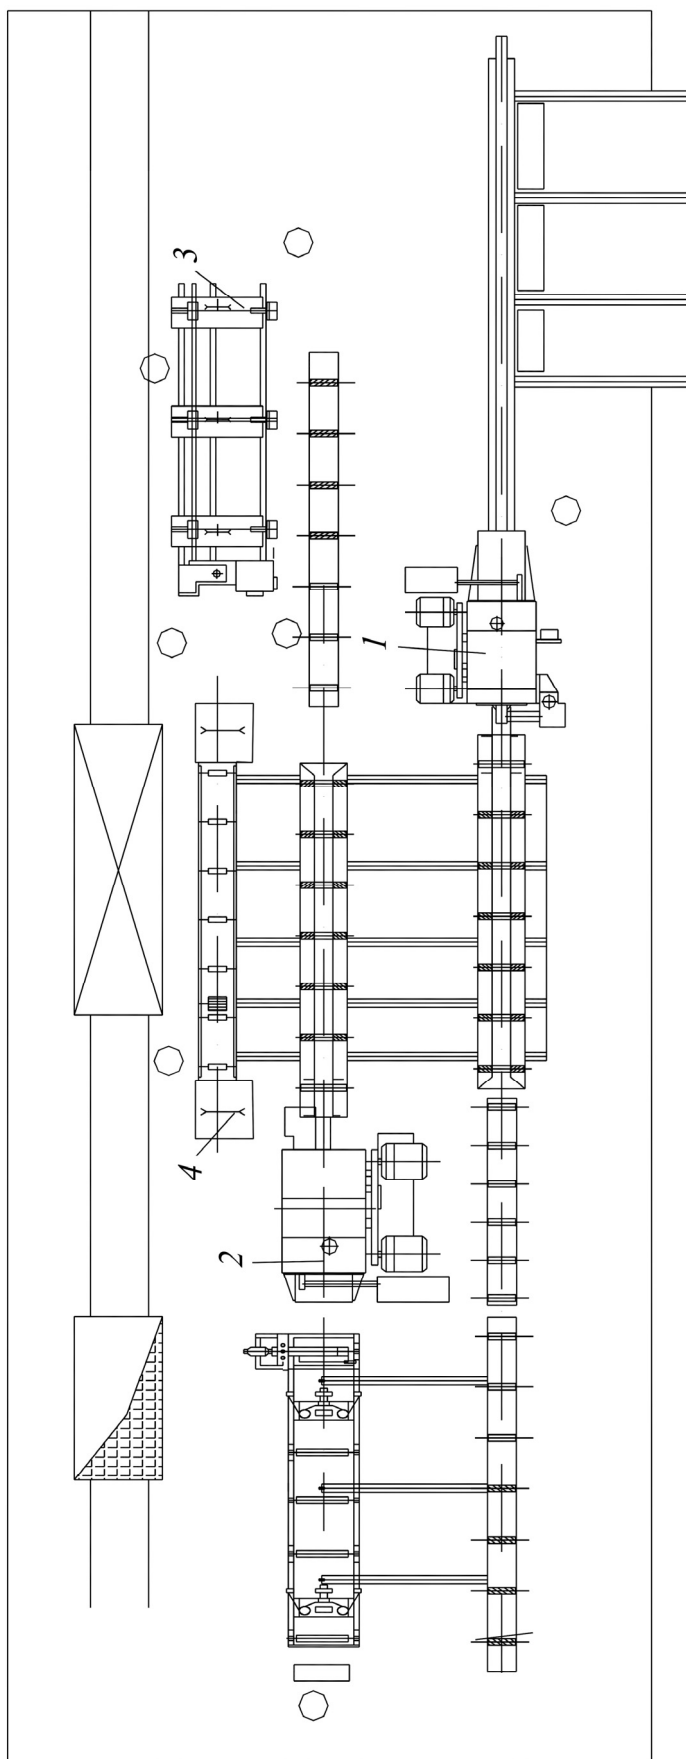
Схема расположения оборудования в цехе на базе многопильных круглопильных станков:
